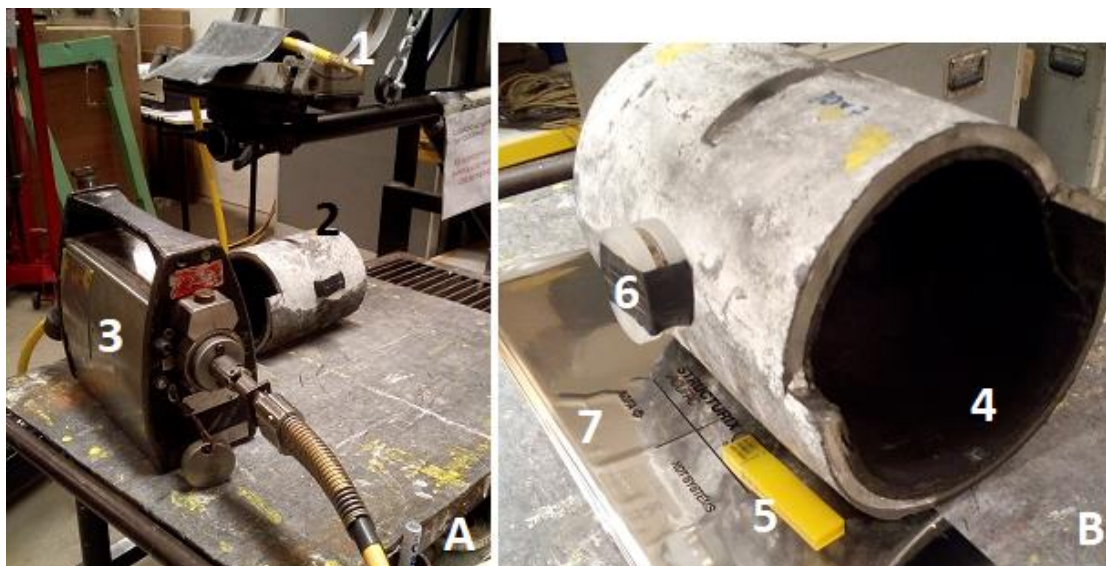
Montagem experimental, (A) 1- Ponteira; 2- Tubo; 3- Equipamento de raios gama; (B) 4- Coque; 5- IQI; 6- Comparador; 7- Filme.
